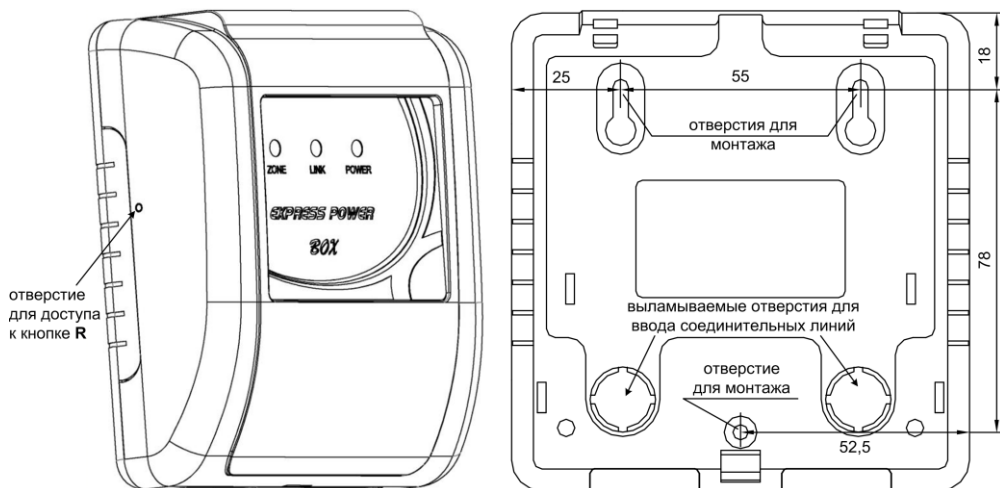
Внешний вид GSM устройства. Присоединительные размеры
